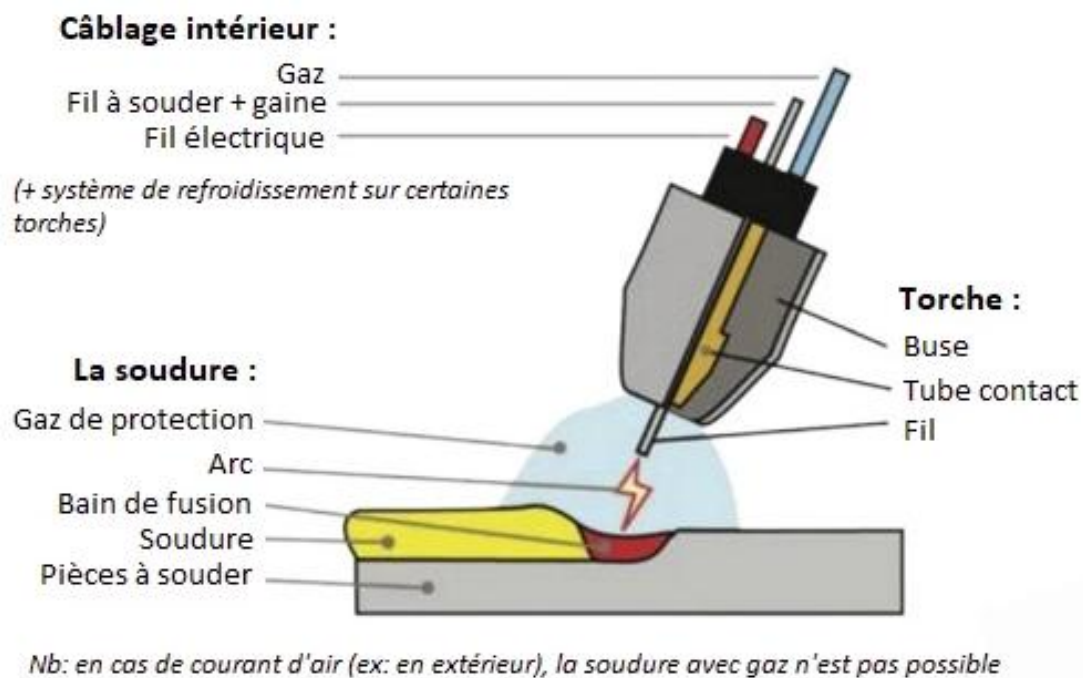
Schéma de soudage MIG/MAG [9]
